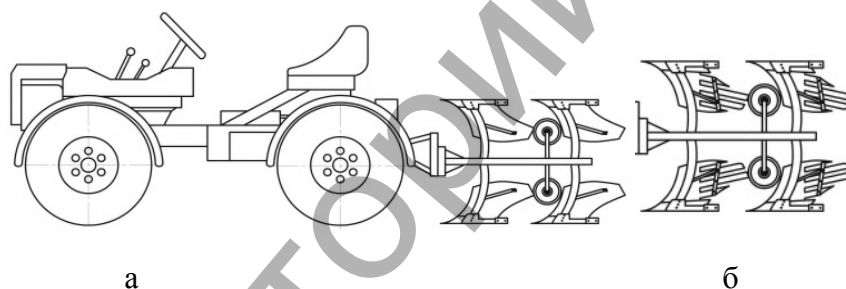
Мини-трактор + оборотный плуг с цилиндрическим (а) и пластинчатым отвалом (б)
